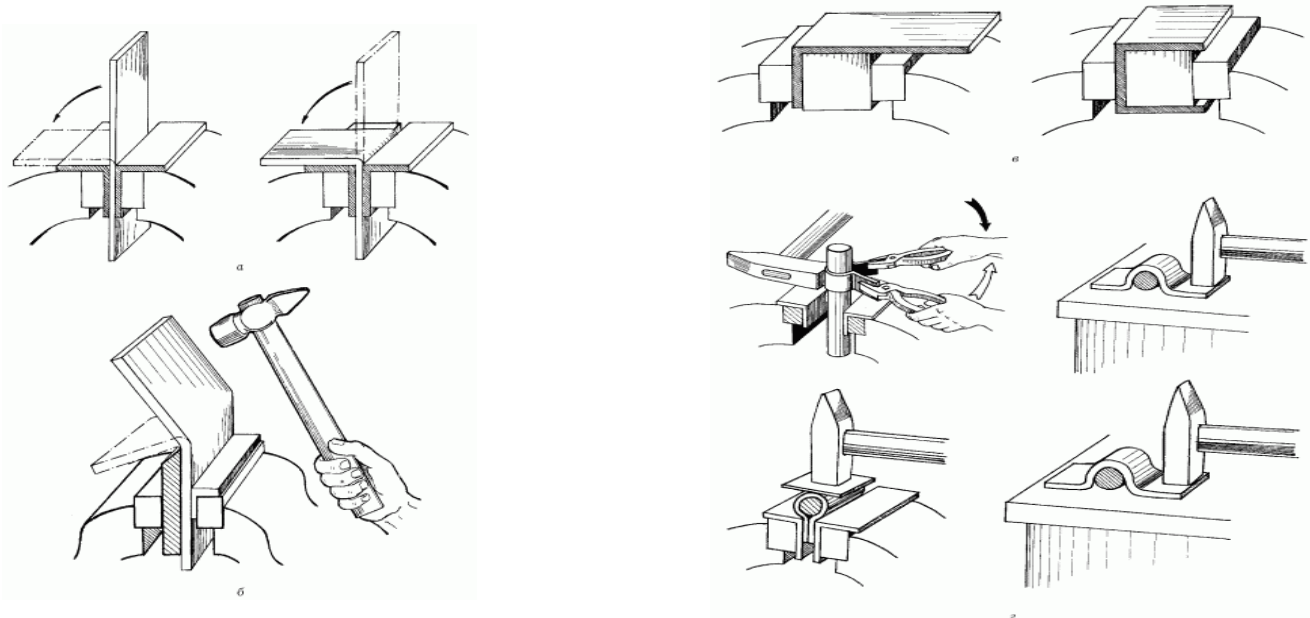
Приемы гибки полос: а – порядок гибки; б – гибка острого угла. в – изготовление скобы; г – изготовление хомутика.
